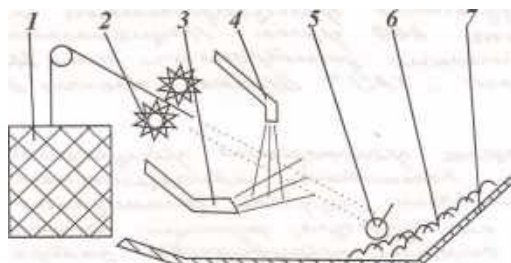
Принципова схема процесу напилювання: 1 – ролинг; 2 – різальний пристрій; 3 – смола із прискорювачем; 4 – смола з каталізатором; 5 – валик; 6 – наповнений шар композиції; 7 – форма
